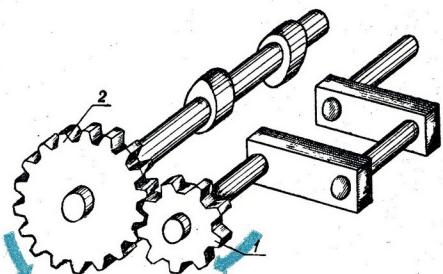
Привод распределительного механизма: 1 — зубчатое колесо, 2 — зубчатое колесо распределительного валика.
